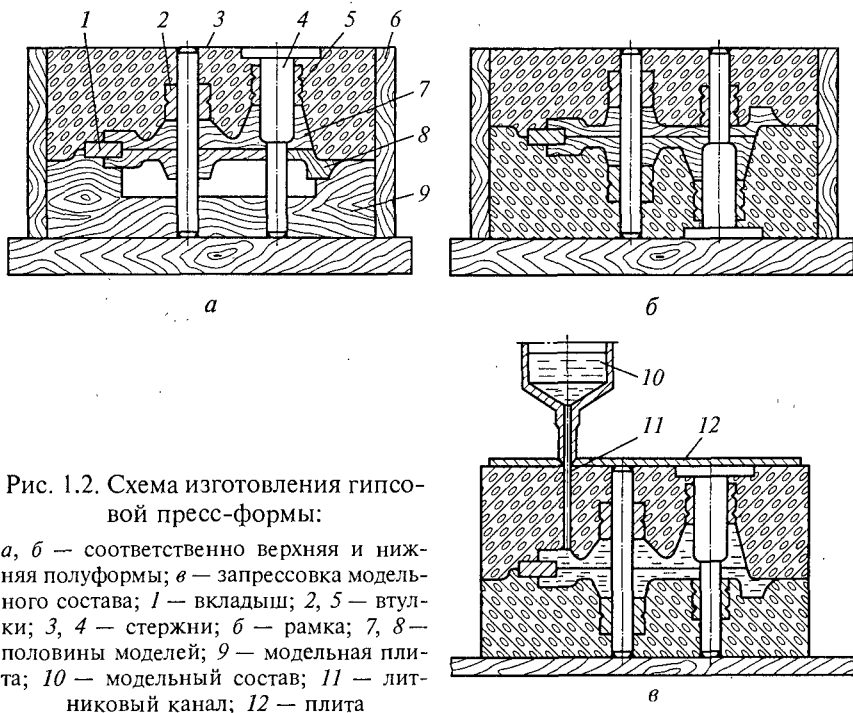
Схема изготовления гипсовой пресс-формы:
